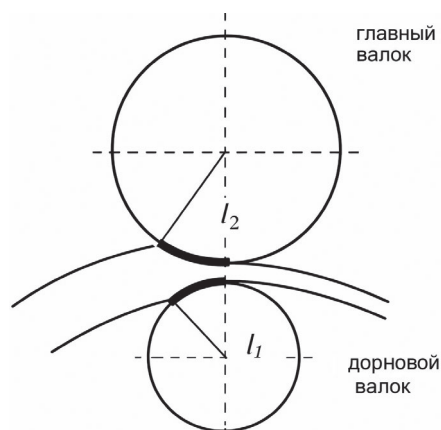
Зоны l_1 и l_2 контакта кольцевой заготовки с дорновым и главным валками
